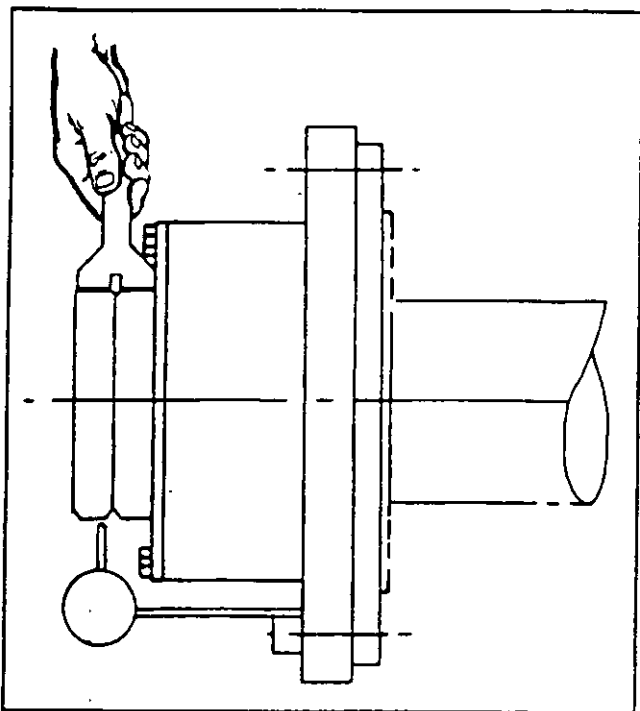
MEDICION DEL ALINEAMIENTO AXIAL DEL COPE ENGRANADO CON UN MEDIDOR. E-32864-S
